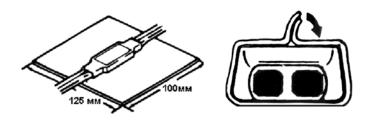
Защита соединителя UDW2 лентой ВМ.
